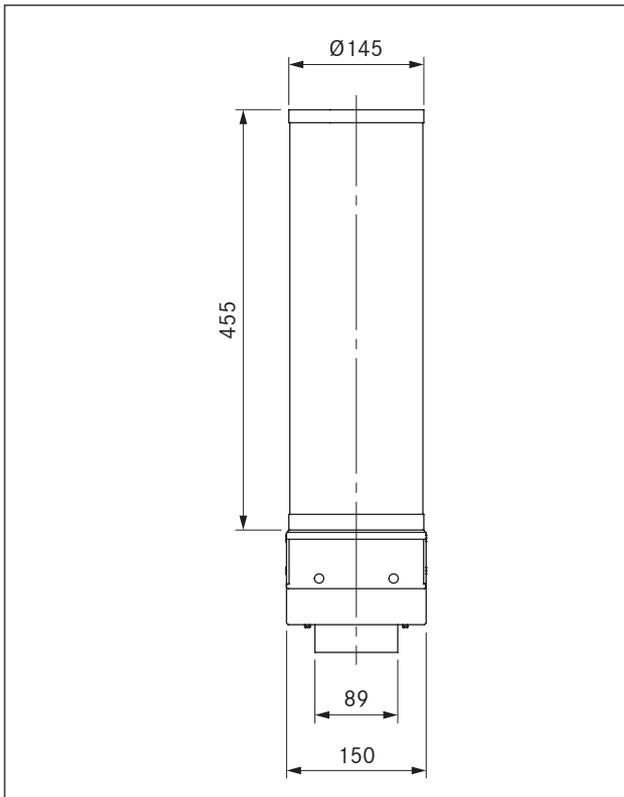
ULB3 dimensiones del aparato vista lateral
